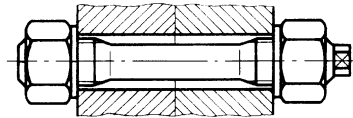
Schraubenverbindungen mit Dehnschaft (langes Gewinde) und Sechskantmutter in Regelform (für M 12 bis M 52); der Schraubenbolzen zentriert die Schraubverbindung
